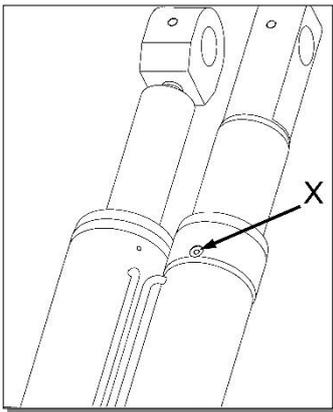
Pos. X = Entlüftungsschraube jeweils an den Folgezylindern
